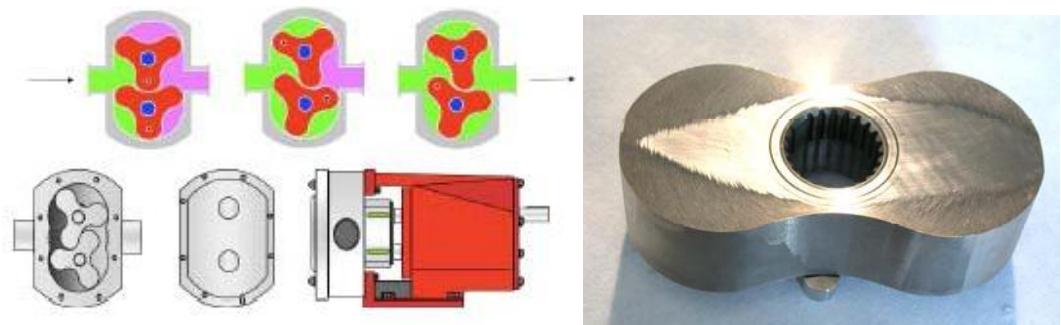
Positiv-pumpe, rotary lobe. Eksempel på rotor, der i testopstilling har været utsat for rivning.
